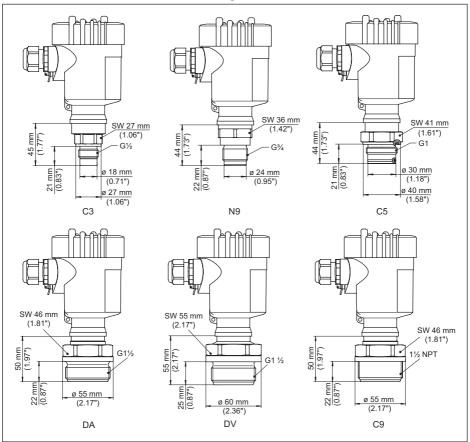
VEGABAR 82, Gewindeanschluss frontbündig
